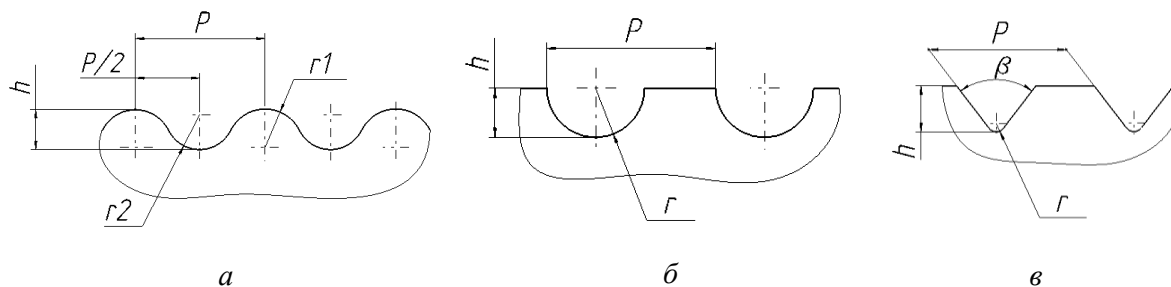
Профили зуба фрезы с криволинейной режущей кромкой типов *NR* (а), *NF* (б) и «Стружколом» (в)
